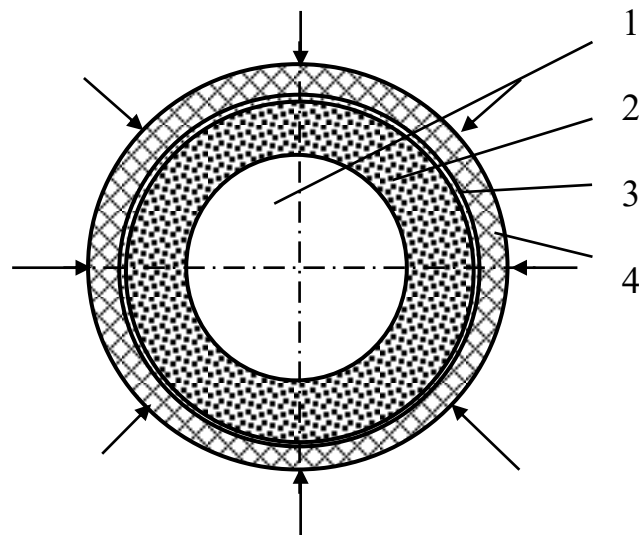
Схема виготовлення шару ППМ: 1 – оправка; 2 – керамічний шар; 3 – прошарок; 4 – оболонка
